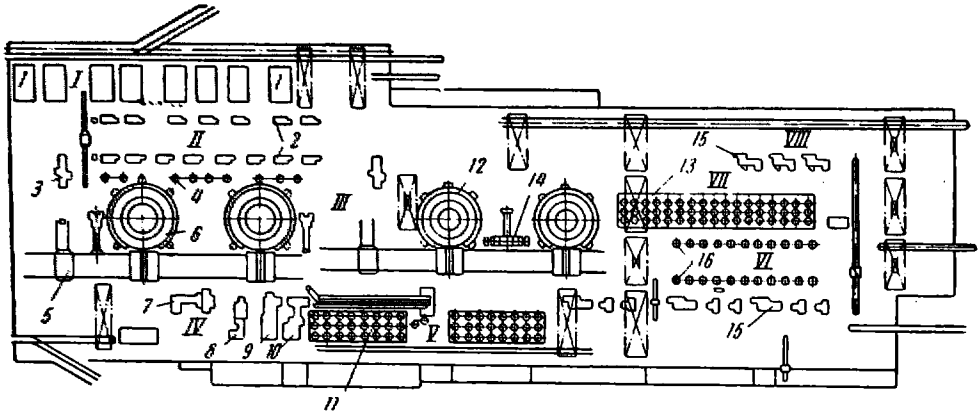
Схема расположения оборудования колесопрокатного цеха: I — склад слитков; II — слиткорезное отделение; III — печное отделение; IV — прессово-прокатное отделение; V — отделение термической обработки; VI — колесоотделка; VII — отделение термической обработки; VIII — отделение приемки и сортировки; 1 — стеллажи для слитков; 2 — слиткорезные станки; 3 — слитколоматель; 4 — карусельные станки; 5 — посадочная машина; 6 — кольцевые печи для нагрева заготовок; 7 — парогидравлический пресс усилием 30 Мн (3000 тс); 8 — парогидравлический пресс усилием 70 Мн (7000 тс); 9 — колесопрокатный стан; 10 — пресс усилием 25 Мн (2500 тс); 11 — печи (колодцы) изотермической выдержки; 12 — кольцевые печи для нагрева под закалку; 13 — печи (колодцы) для отпуска; 14 — закалочные столы; 15 — столы осмотра; 16 — карусельные стянки
